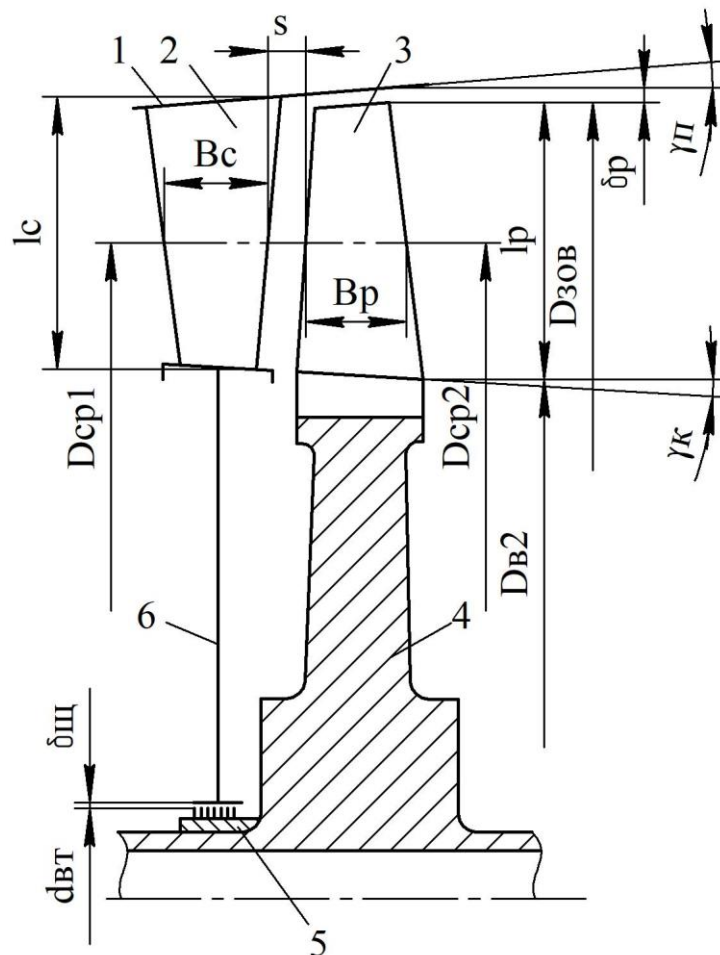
Схема ступеня ТНТ: 1 – корпус турбіни; 2 – соплова лопатка; 3 – робоча лопатка; 4 – диск турбіни з валом; 5 - ущільнення діафрагми; 6 – діафрагма.
